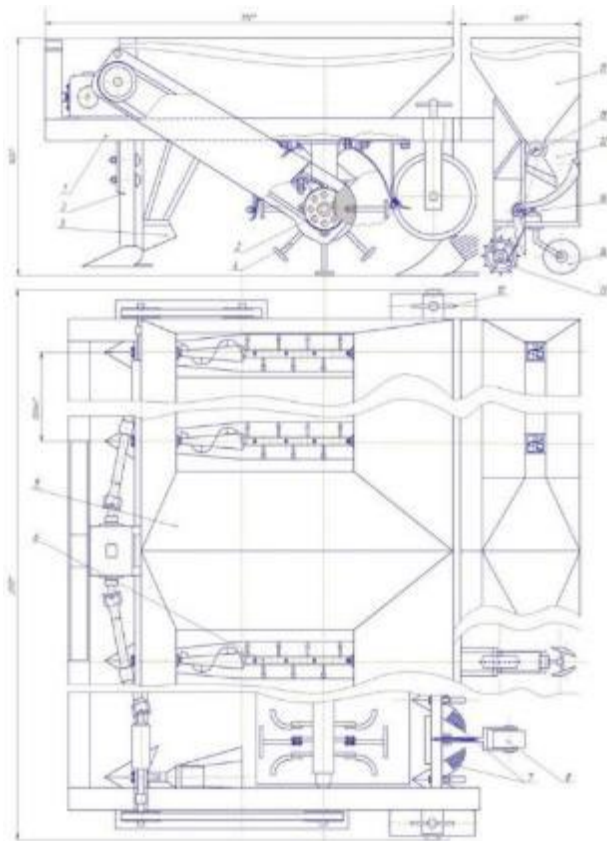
Універсальна машина для вирощування органічної картоплі: 1- рама; 2 – фреза; 3 – сошники; 4 – ножі; 5 – труба; 6 – механізм подачі добрив; 7 – підгортач; 8 – ущільнювач; 9 – бункер добрив; 10 - опорне колесо; 11 – бункер картоплі; 12 – садильний апарат; 13 – загортач; 14 – мірне колесо; 15 – дозатор; 16 - катушка
